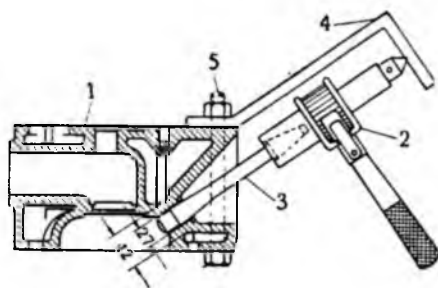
Приспособление для ремонта отверстия свечи в головке блока с испорченной резьбой (в рабочем положении):
